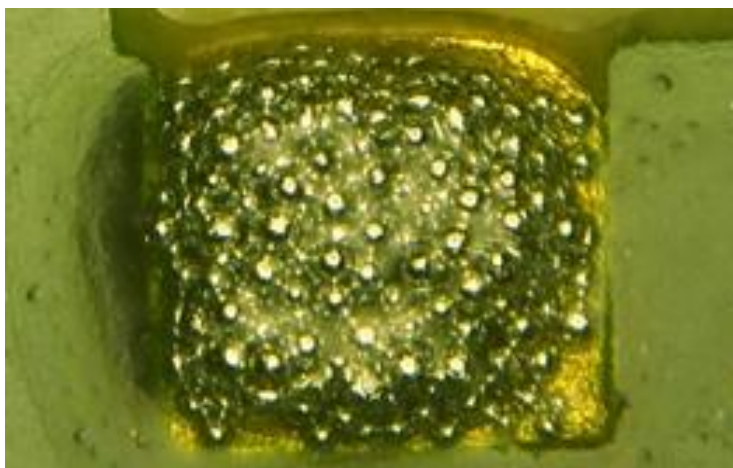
Impresión de soldadura de pasta usando soldadura tipo V
